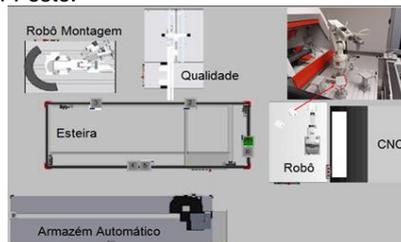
Layout da planta do laboratório iCIM-Festo (Fonte: Fatec-So, 2020).
